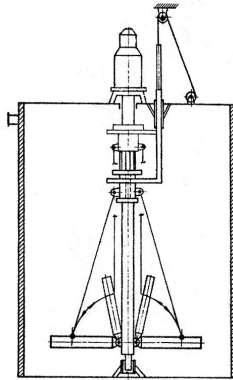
Лопатева мішалка згідно з а. с. № SU1720697A1
